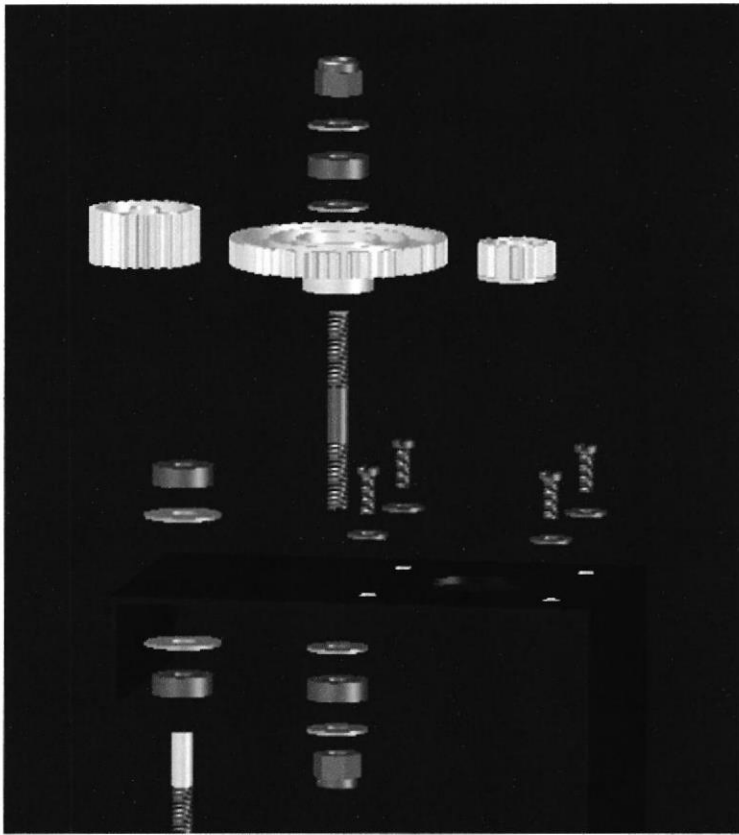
Vista superior de la pieza que sujeta al motor del eje Z con su juego de engranes y piezas de sujeción.
